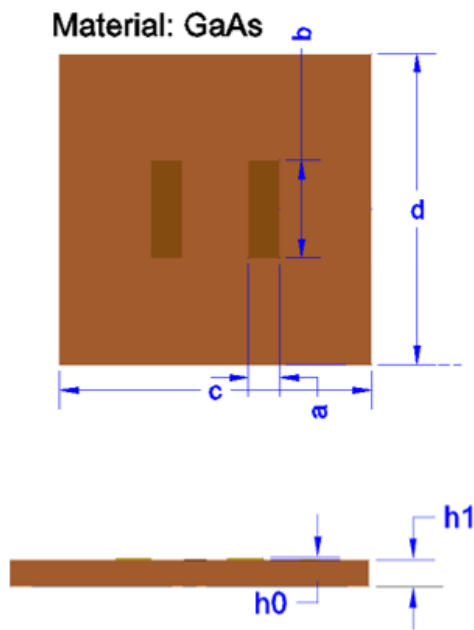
Vista superior y vista frontal de las dimensiones de la tierra
